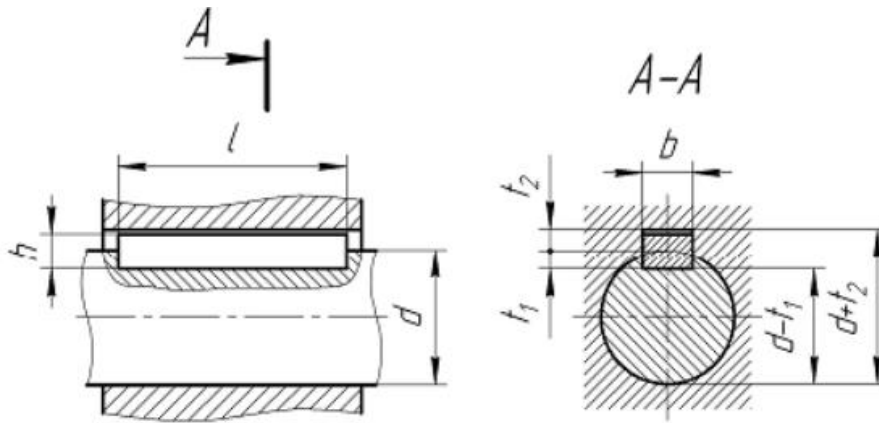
Розрахункова схема з'єднання призматичною шпонкою
